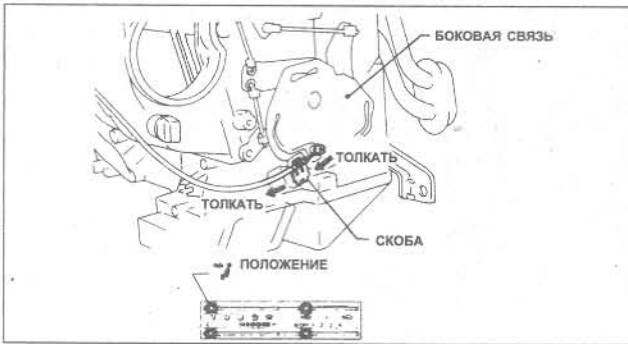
Регулировка тросика рычага управления потоком воздуха (Глава 39)
